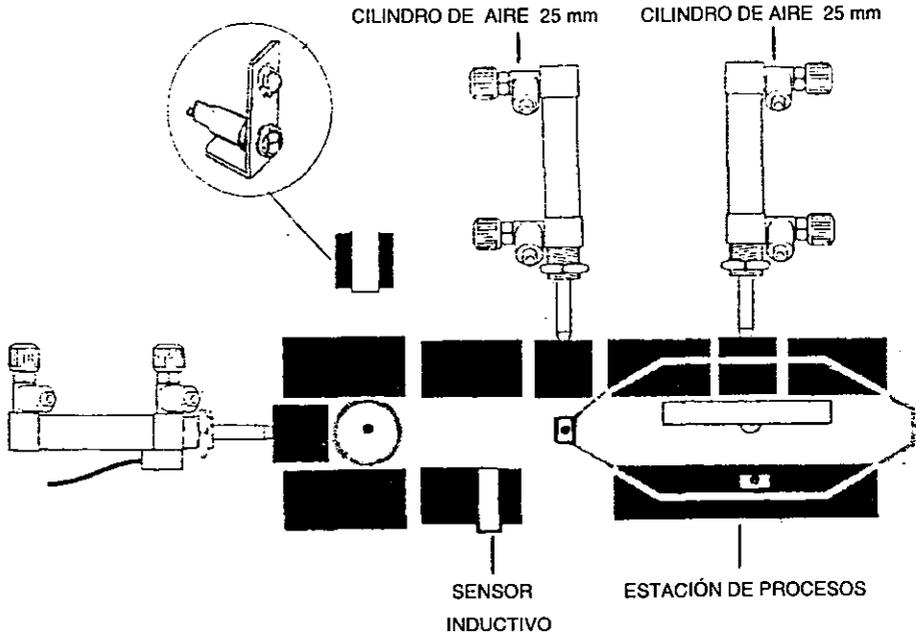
Vista en planta del ensamblaje de módulos hasta el párrafo 8.
